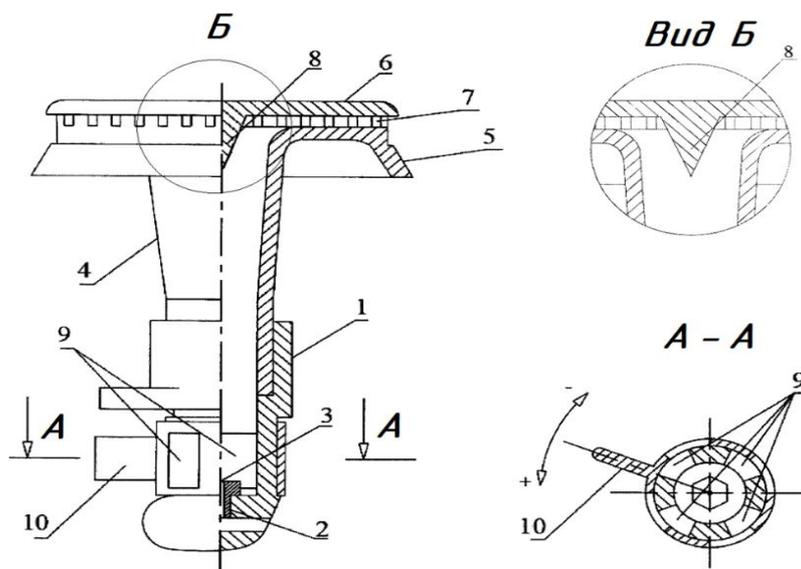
Конструкция газогорелочного устройства: 1 – корпус; 2 - газовое сопло; 3 - аксиальное выходное отверстие; 4 – смеситель; 5 – выходной торец смесителя; 6 – крышка; 7 – огневые отверстия; 8 – тепловой рассекатель; 9 – отверстия подачи первичного воздуха; 10 – регулятор подачи первичного воздуха
